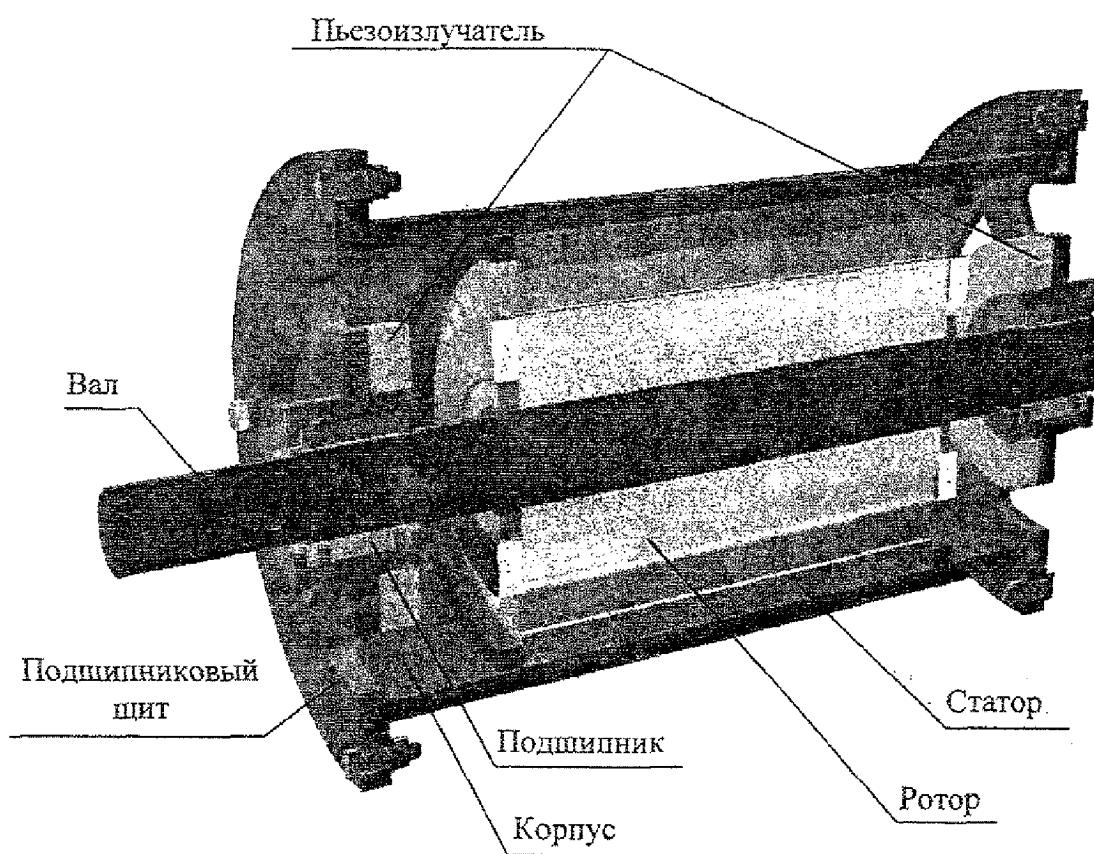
Схема размещения пьезоизлучателей на подшипниковых щитах ПЭД
